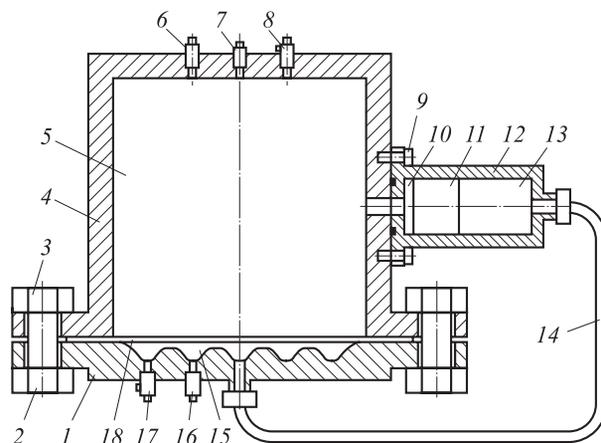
Схема устройства для листовой газовой штамповки с односторонним нагревом заготовки
